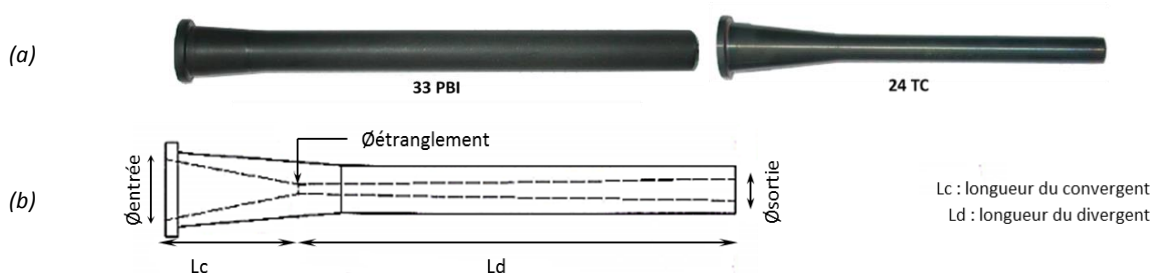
Schéma d'une buse cold spray (a) vue extérieure (b) vue en coupe, voir les dimensions dans le Tableau 2-5.
